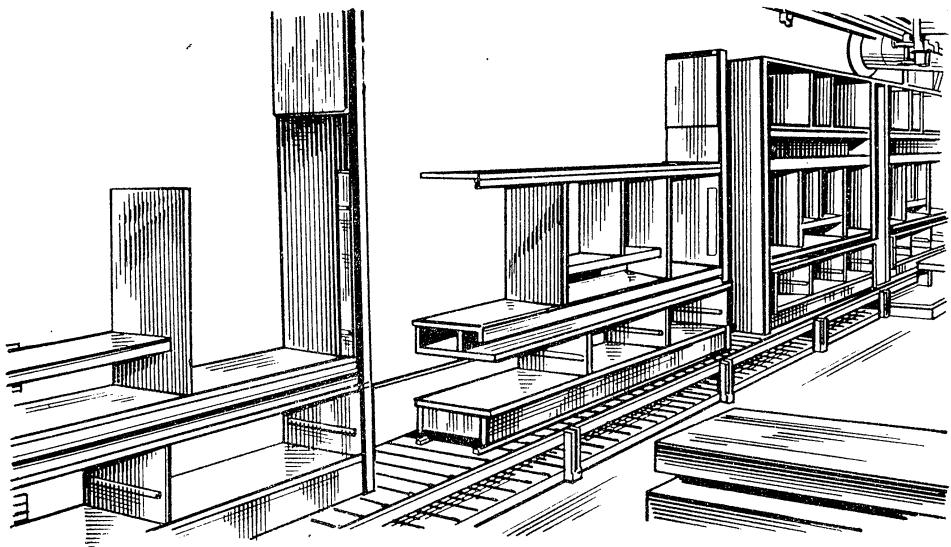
Сборка корпусной мебели на приводном пластинчатом конвейере
